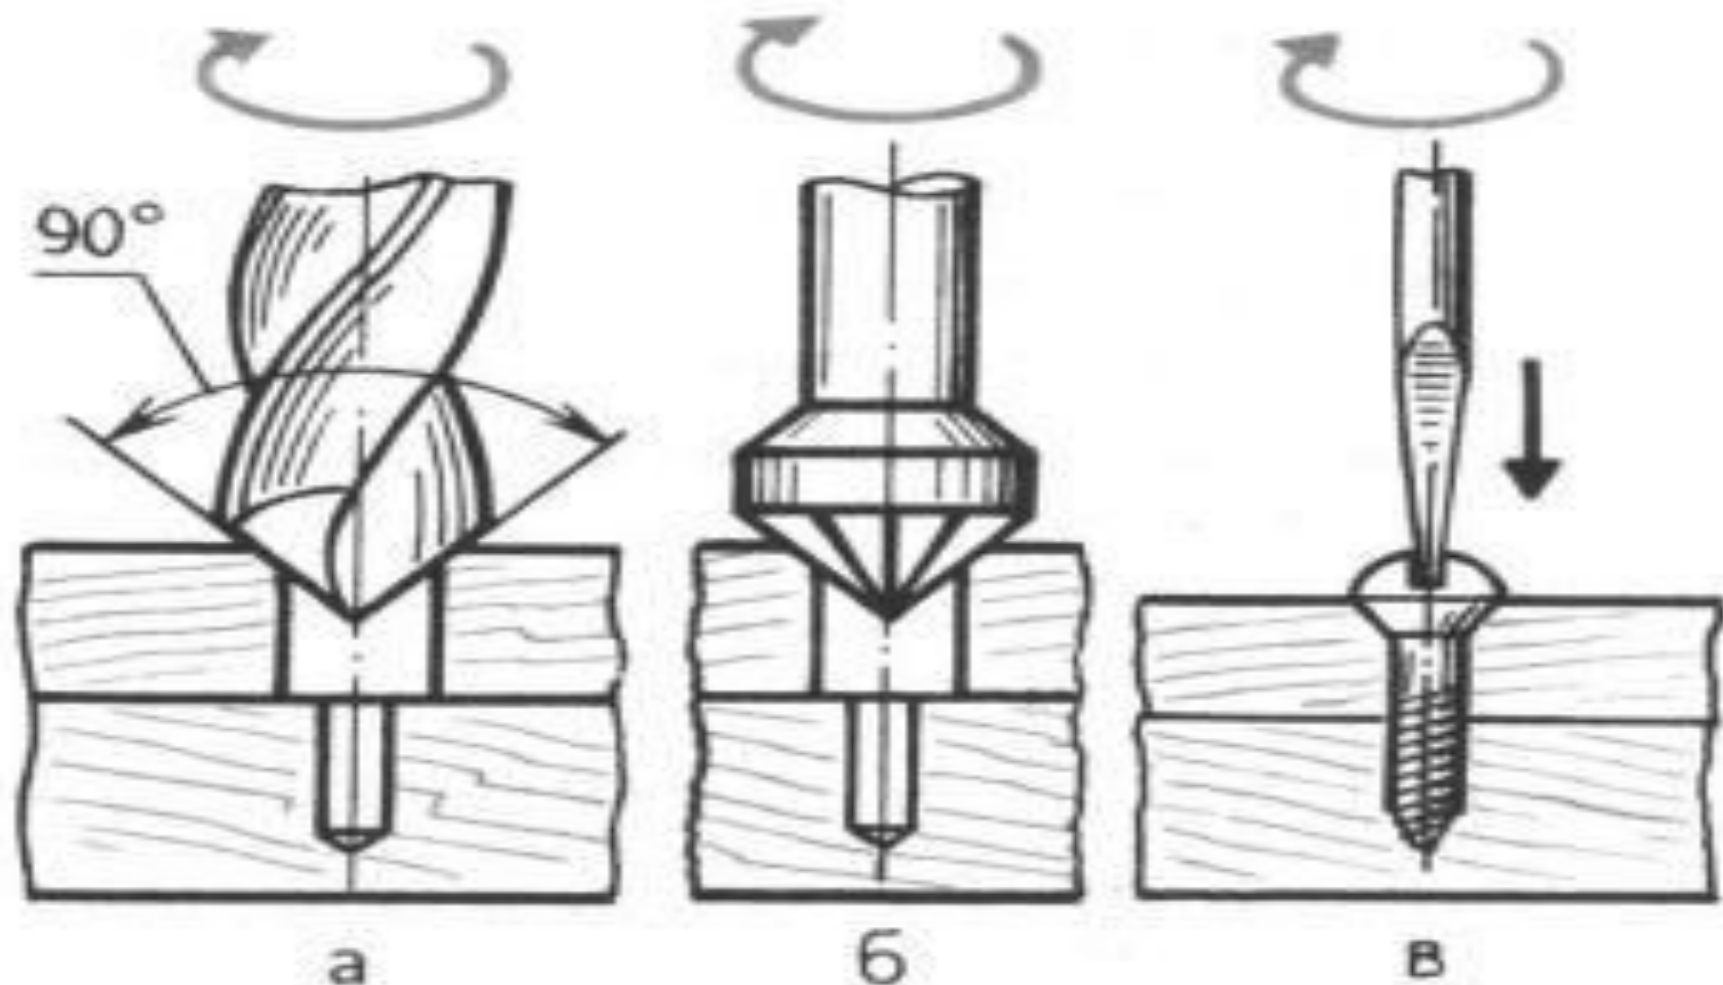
Подготовка гнезда под головку шурупа сверлом (а) и зенковкой (б) и ввинчивание шурупа отверткой (в)
